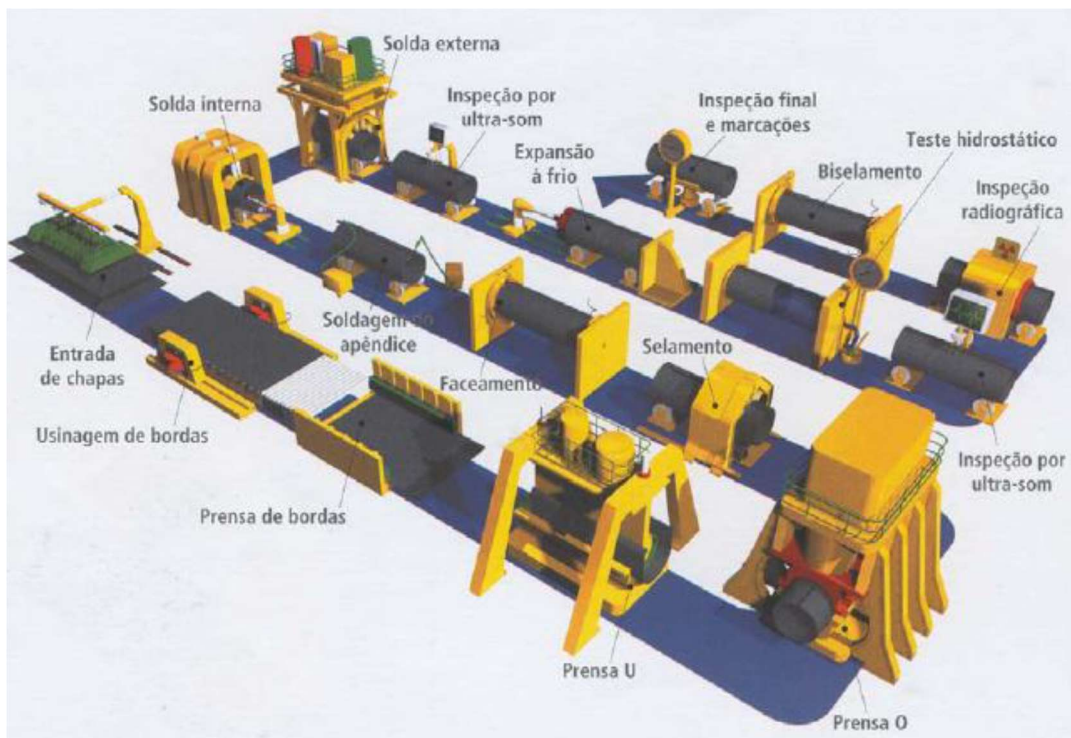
Rota de fabricação UOE de soldagem de tubos com costura longitudinal (HIPPERT, 2004).
